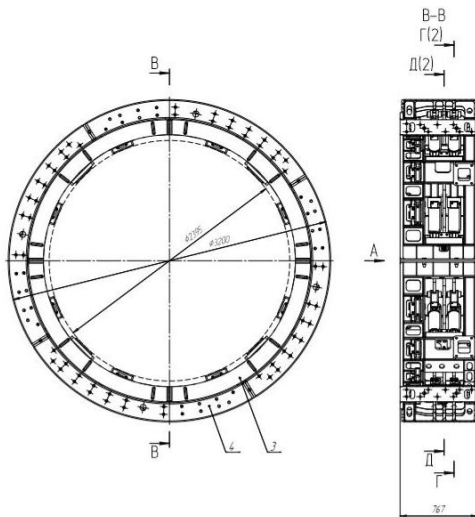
Фрагмент сборочного чертежа УСС опытного образца геолода диаметром 3,2 м
